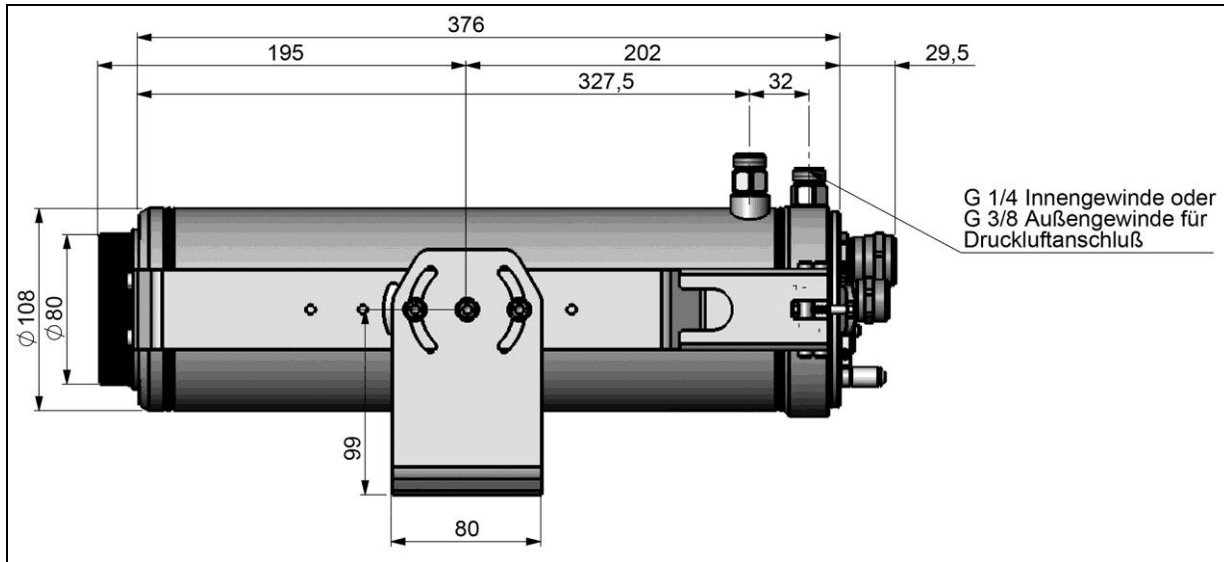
Cooling Jacket Advanced Extended - Seitenansicht
